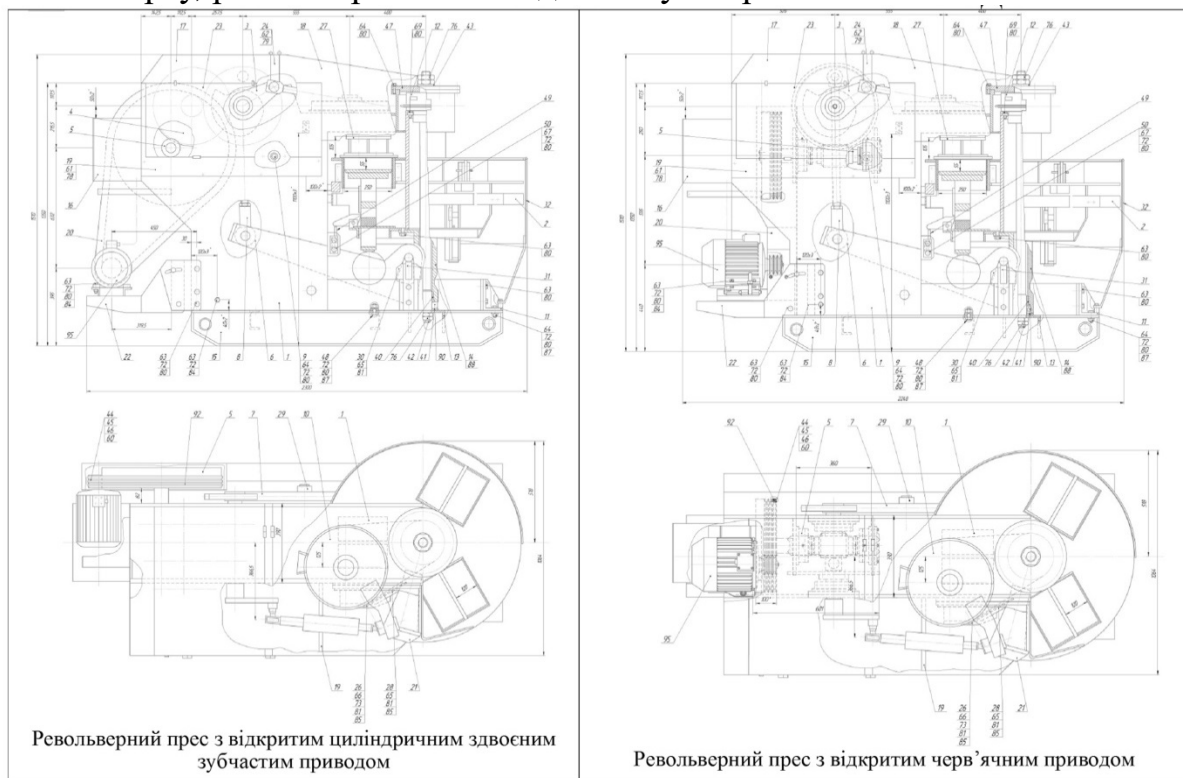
Вид загальний револьверного преса для формування напівфабрикатів керамічної цегли
